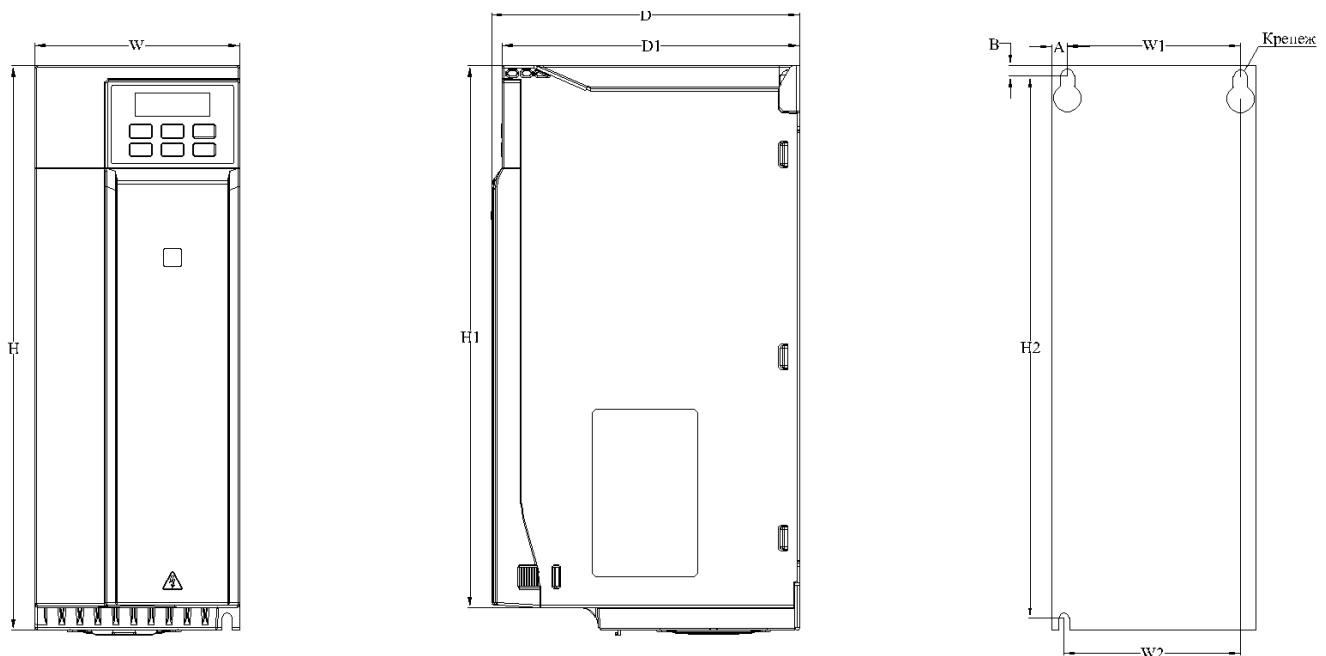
Чертеж преобразователя частоты типоразмер 3
